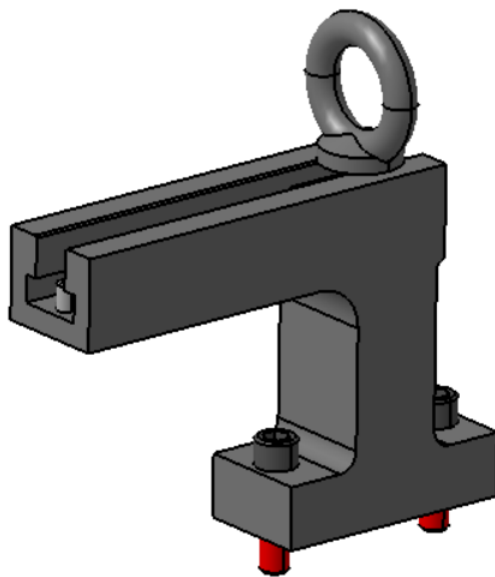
Boční odformování – dvě posuvné kompaktní jednotky Meusburger
